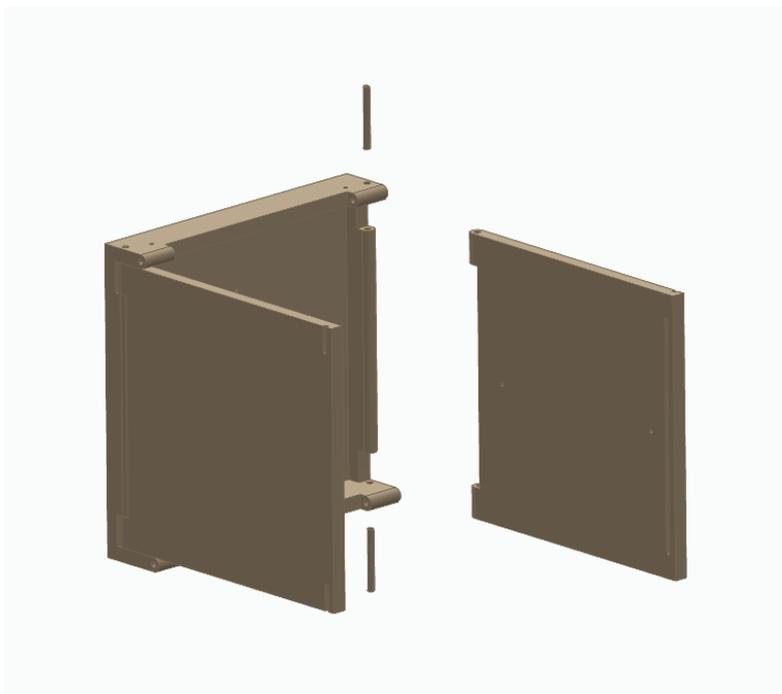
Posicionamiento de tablero derecho e inserción de ejes
